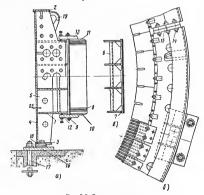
Статор генератора. a — разрез по статору; b — план сегмента статора; b — корпус статора.
